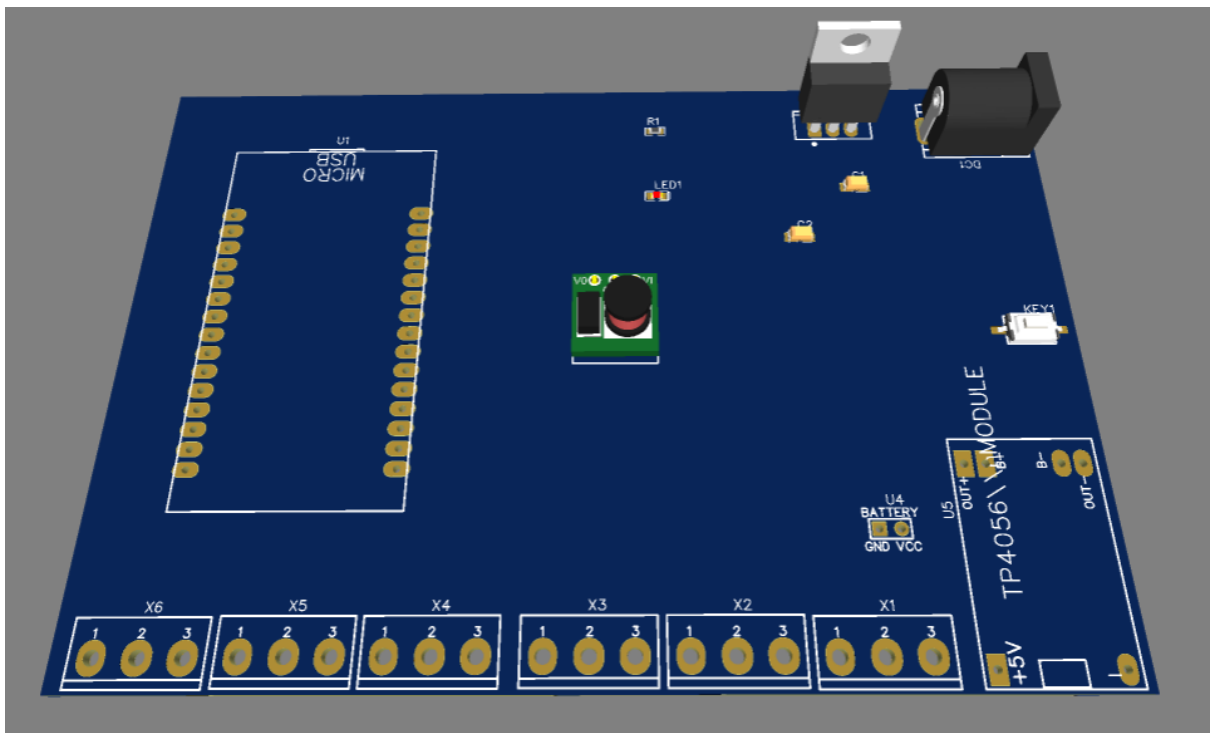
3 D вигляд макетної плати апаратної частини проєктованого засобу
